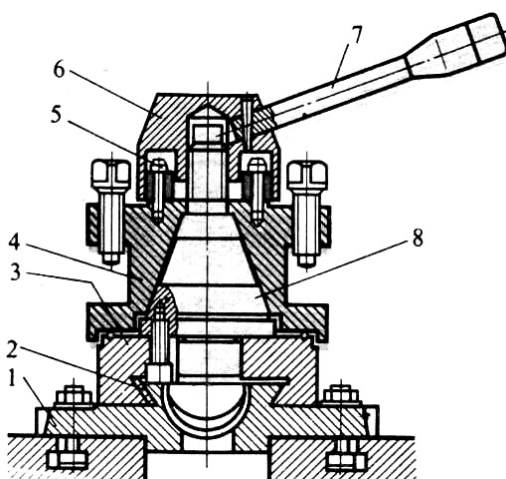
Різцетримач токарно-гвинторізного верстата мод. 16K20
